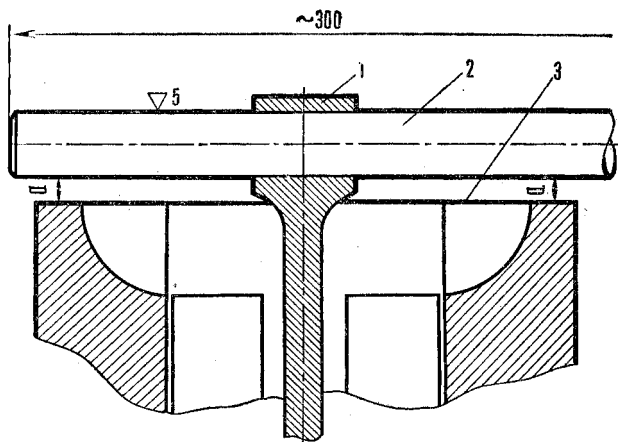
Схема проверки параллельности оси верхней головки шатуна и верхней плоскости картера: 1 — верхняя головка шатуна; 2 — оправка; 3 — верхняя плоскость картера
